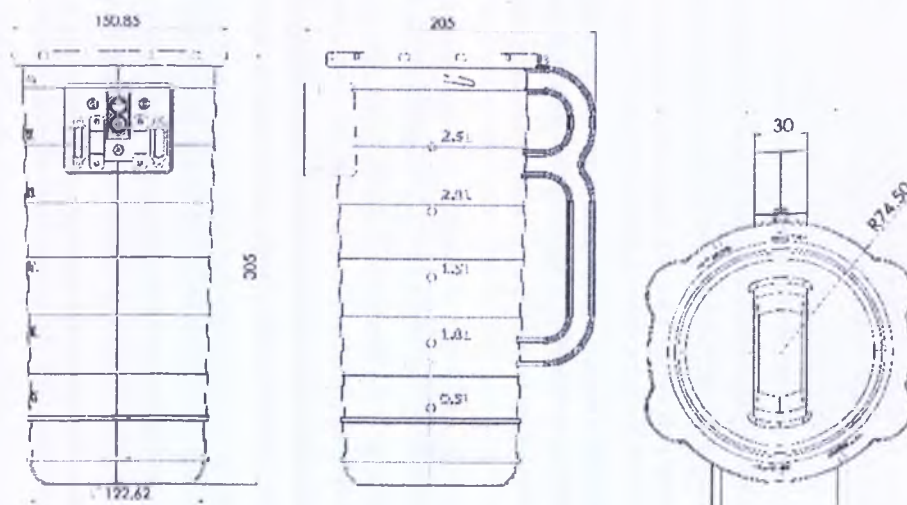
Схематичное изображение и габаритные размеры Контейнера для отходов
